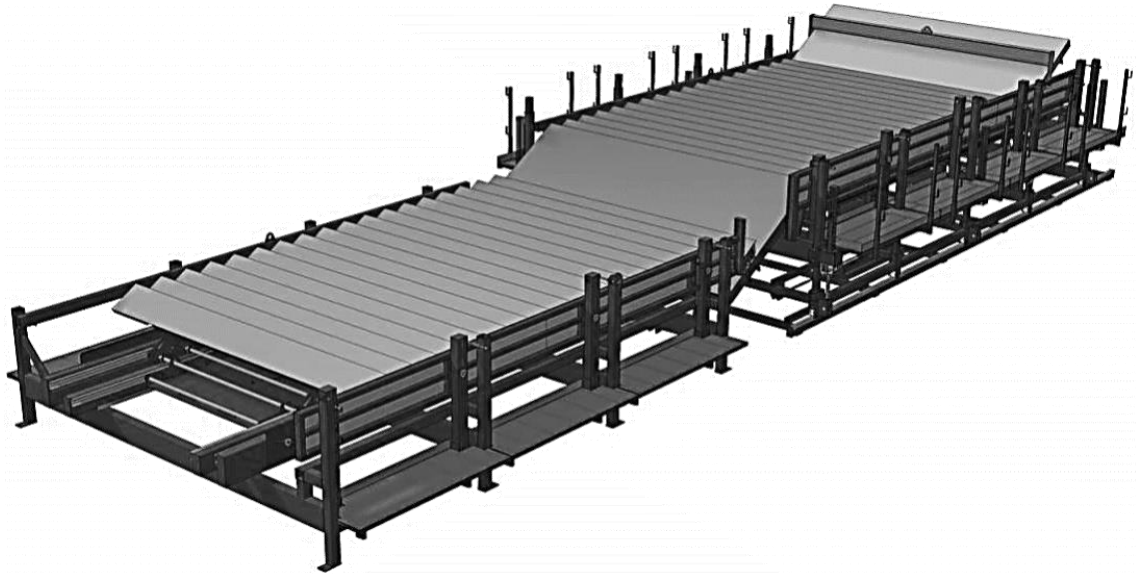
Установка Flexcasters для виготовлення широких маршів
